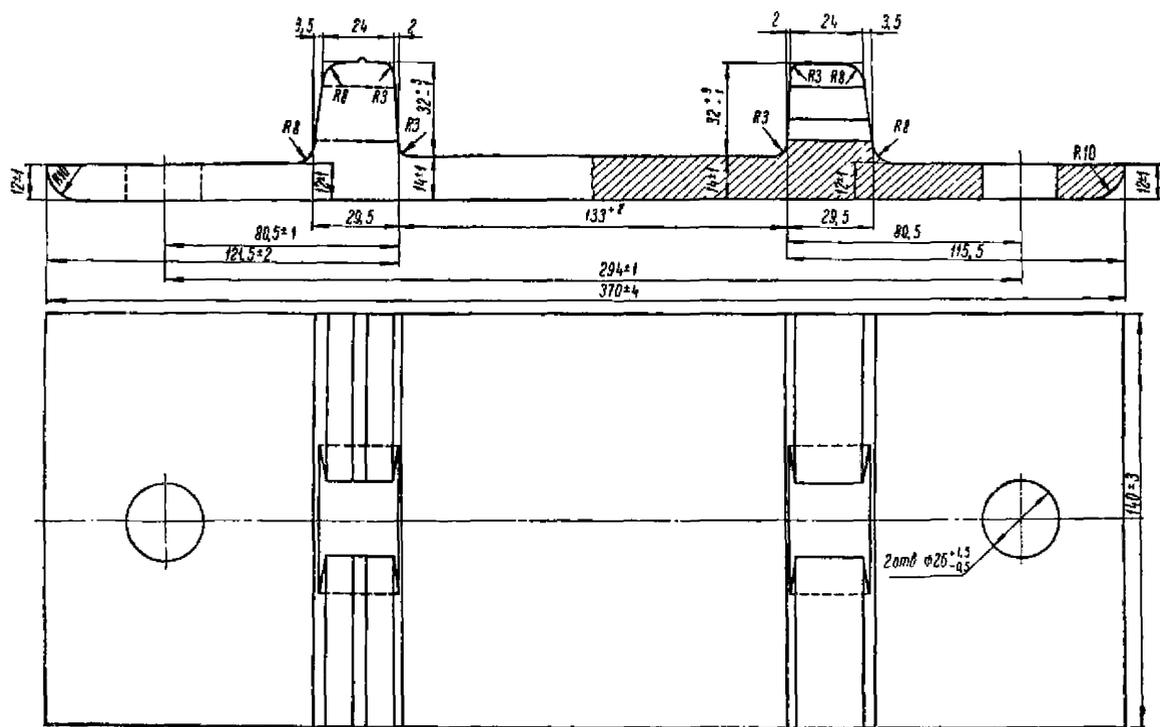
Подкладка марки К плоская с шурупным прикреплением к железобетонной шпале и расположением отверстий для пути с рельсами типа Р50
